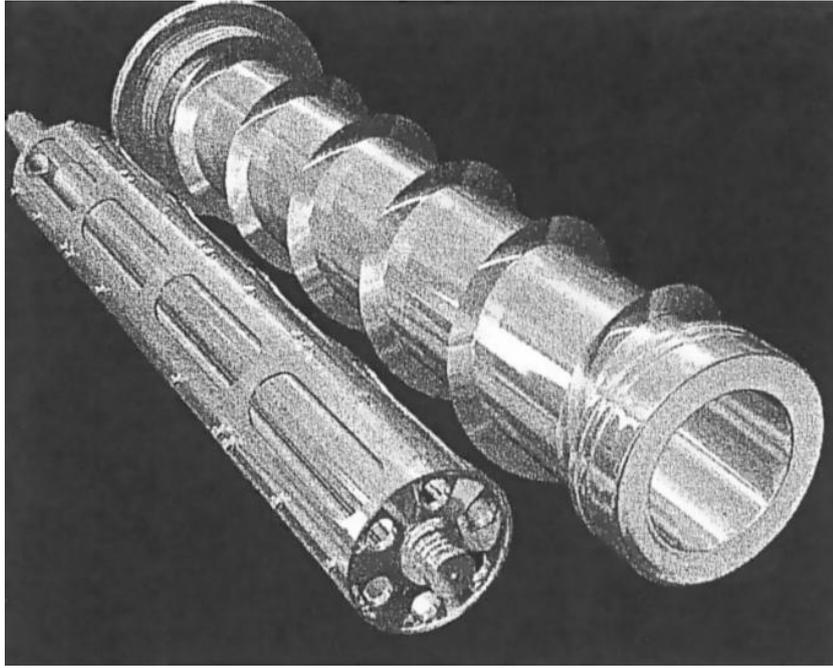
Морозильный цилиндр и мешалка с плавающими ножами скребкового типа
